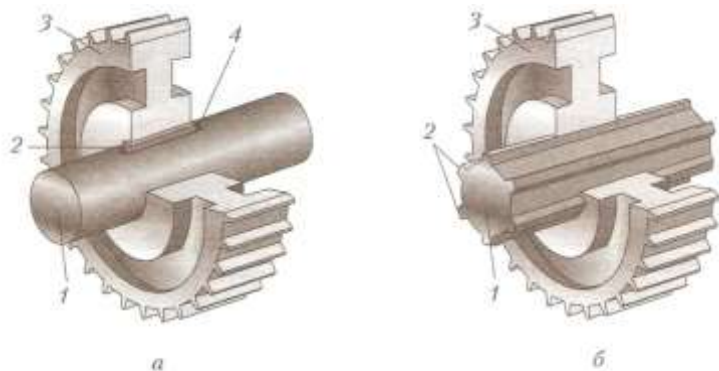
Соединение шестерни с валом: а – шпоночное: 1 – вал; 2 – шпонка; 3 – шестерня; 4 – шпоночный паз; б – шлицевое: 1 – шлицевой вал; 2 – шлицы; 3 – шестерня
